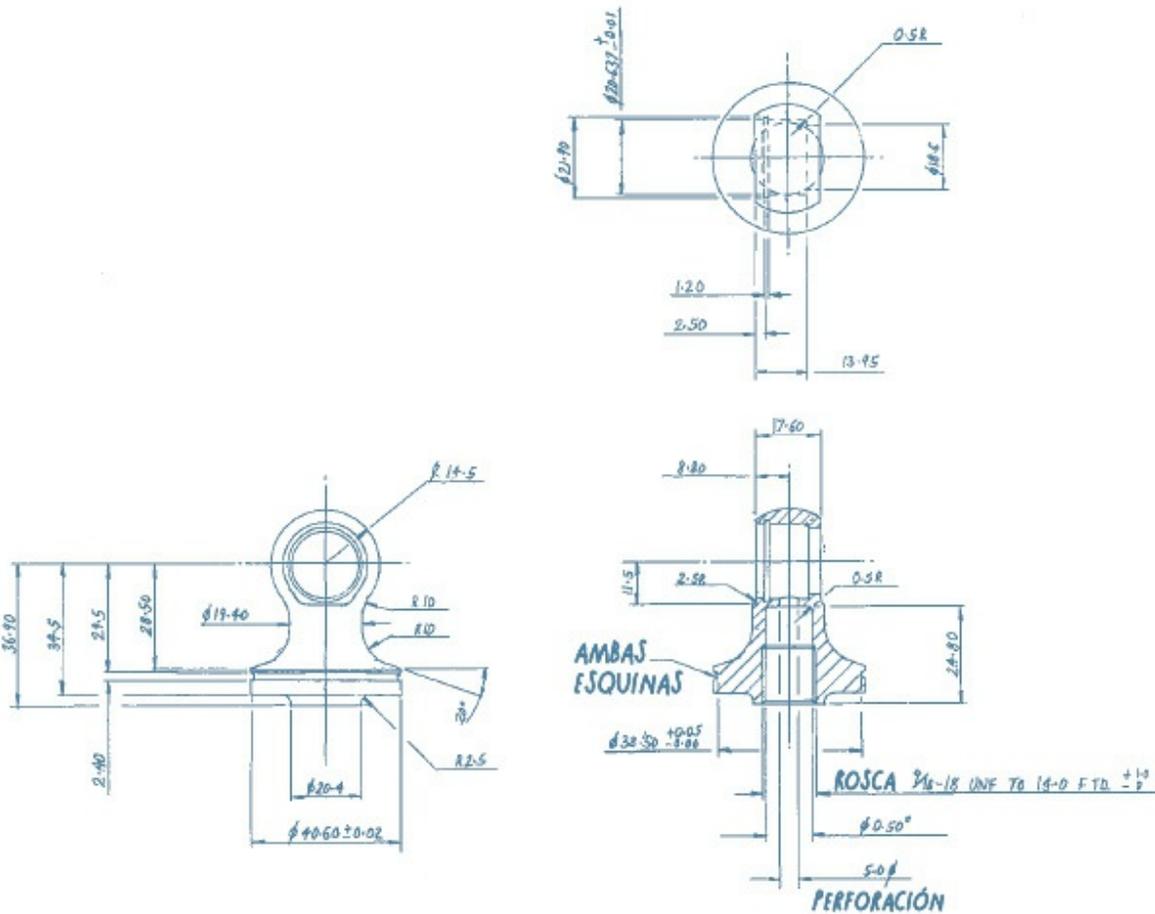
Dibujo técnico de la parte superior del amortiguador trasero del March 86C.
